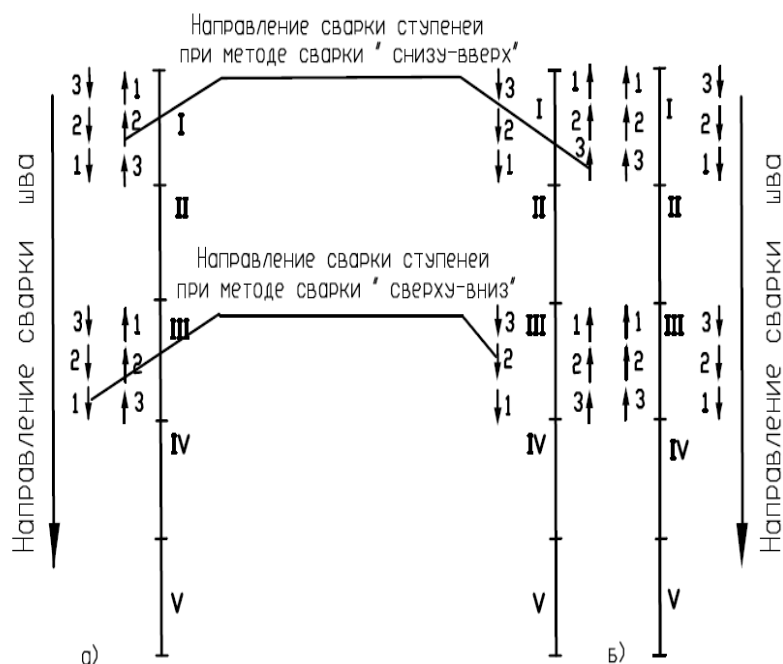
Последовательность сварки прямолинейного шва
